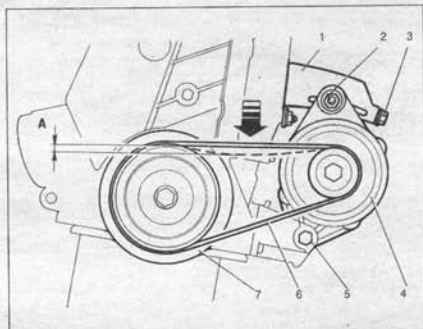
Проверка натяжения ремня привода генератора: 1 – верхний кронштейн генератора; 2 – гайка; 3 – регулировочный болт; 4 – генератор; 5 – болт шарнирного крепления генератора к нижнему кронштейну; 6 – ремень; 7 – ведущий шкив на коленчатом валу
